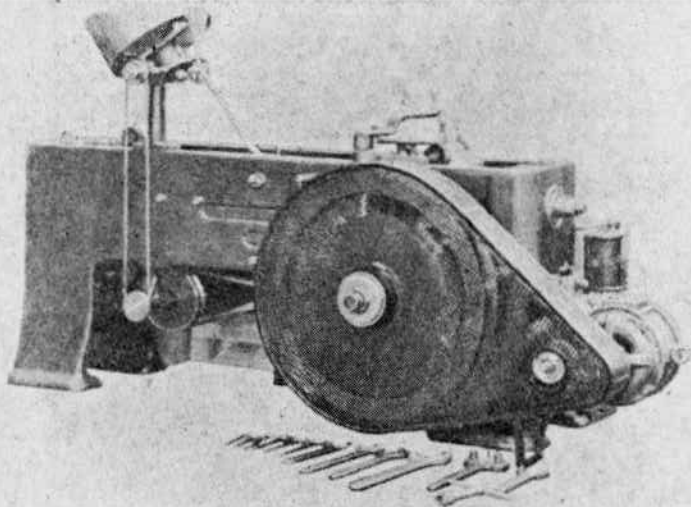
Коленорычажный автомат «Манурен» для высадки колпачков или заготовок большого размера.
